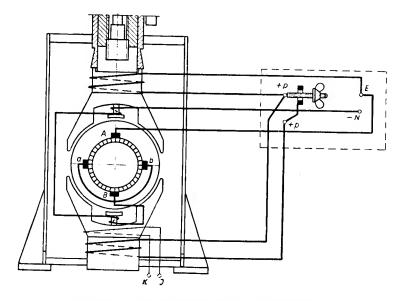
Aufbauskizze des Schweissgenerators
